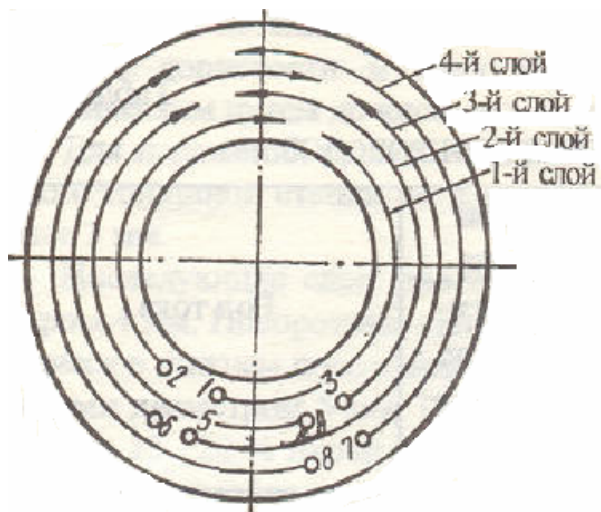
Порядок наложения слоев сварки в сечении трубопровода 1,2,3,4- направление слоев сварки «вразбежку».
